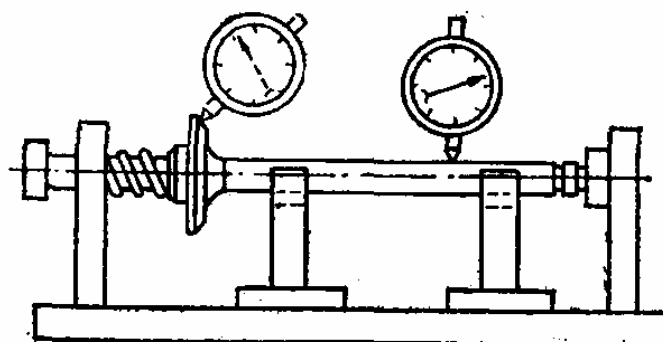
Схема перевірки биття стрижня і робочої фаски клапана, встановленого на призмах
